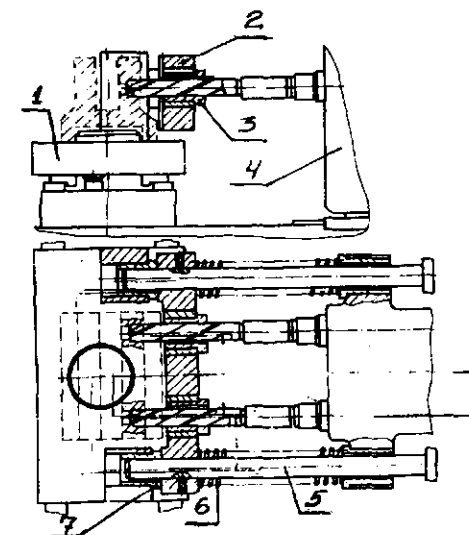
Подвижная кондукторная плита, фиксируемая на приспособлении: 1 – приспособление; 2 – кондукторная плита; 3 – сменная кондукторная втулка; 4 – агрегатная головка; 5 – направляющая штанга; 6 – пружина; 7 – направляющая втулка
